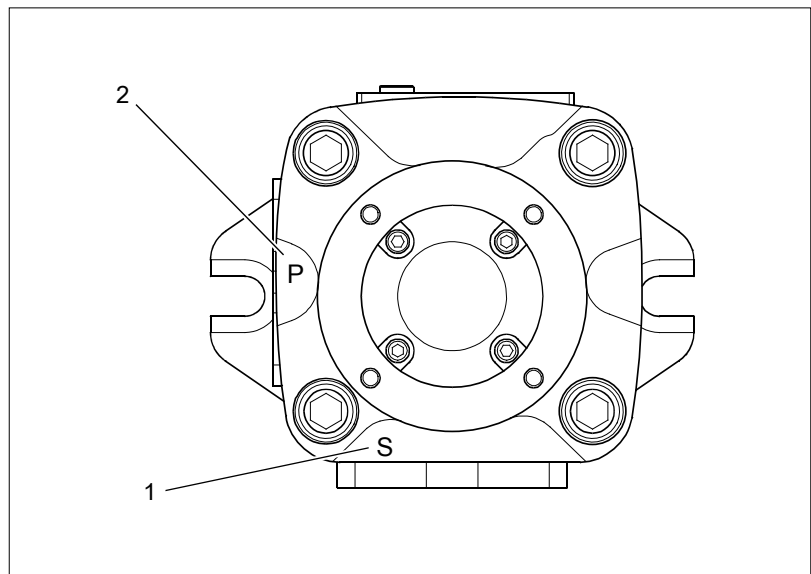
Ansicht Gehäuse mit Kennzeichnung Druck- und Sauganschluss
